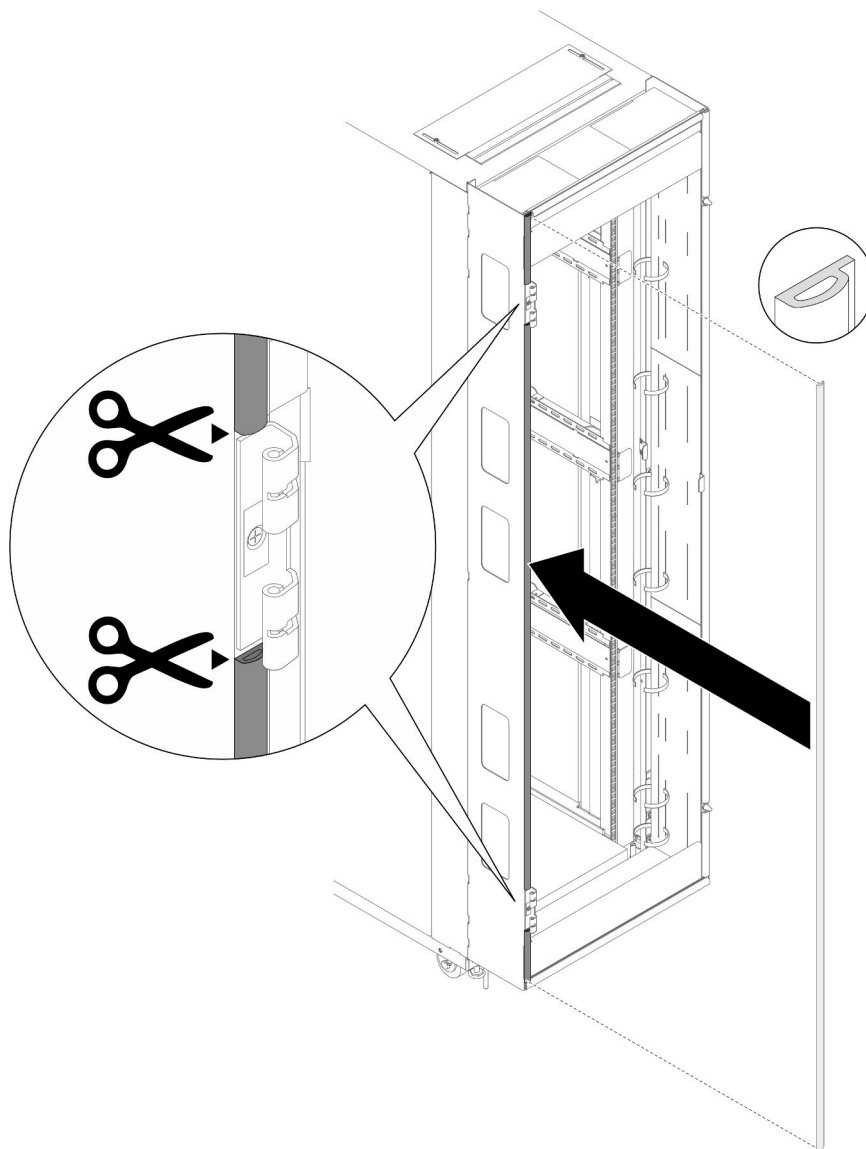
Installation de la mousse d'étanchéité d'extension sur le côté gauche de l'armoire
